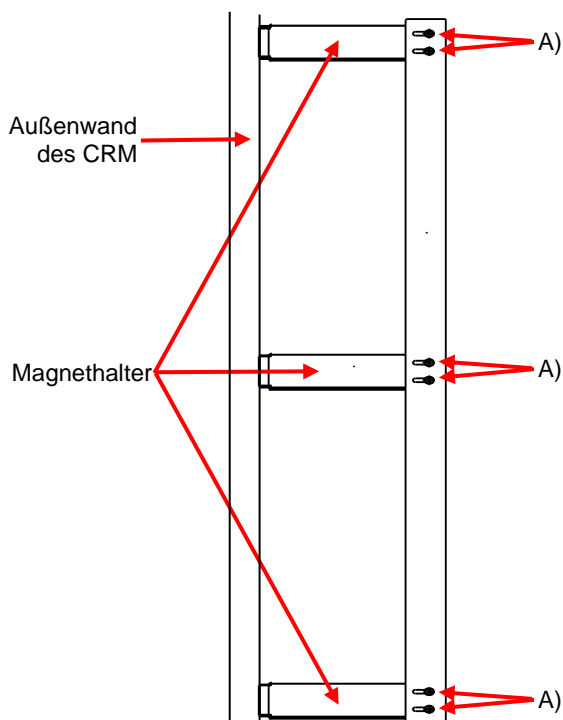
Andrückprofil rechts, Ansicht von hinten
